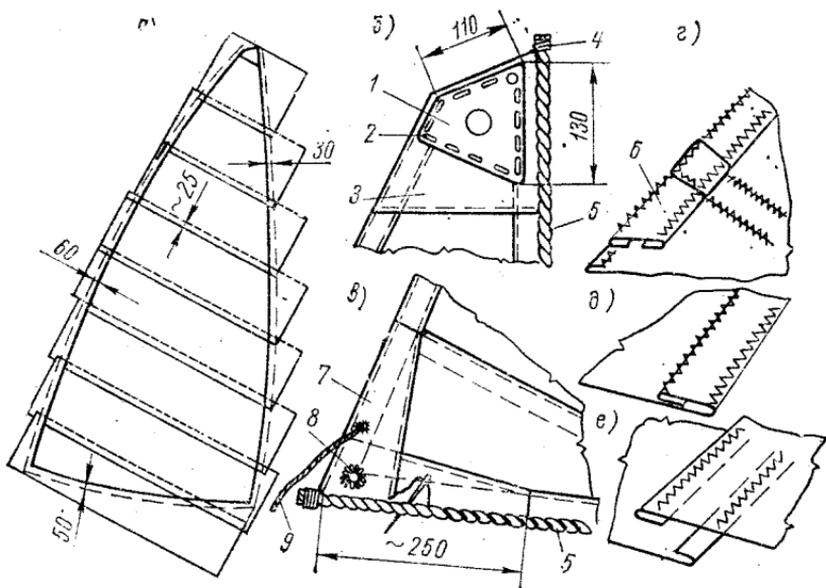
Укладка полотнищ при раскрое паруса (а) и детали конструкции грота; б — фаловый угол; в — шкотовый угол; г — заделка задней шкаторины; д — заделка передней и нижней шкаторин; е — шов, соединяющий два полотнища.
